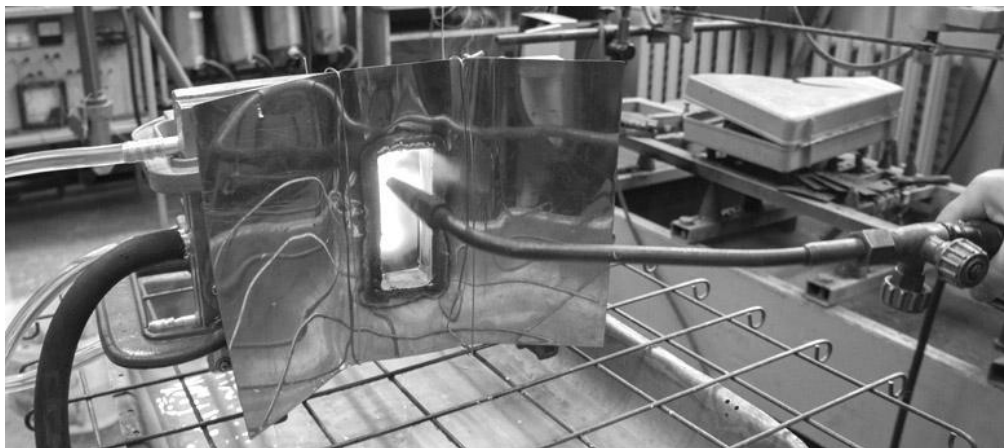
Компоновка обладнання для нагрівання пластини із прорізами
